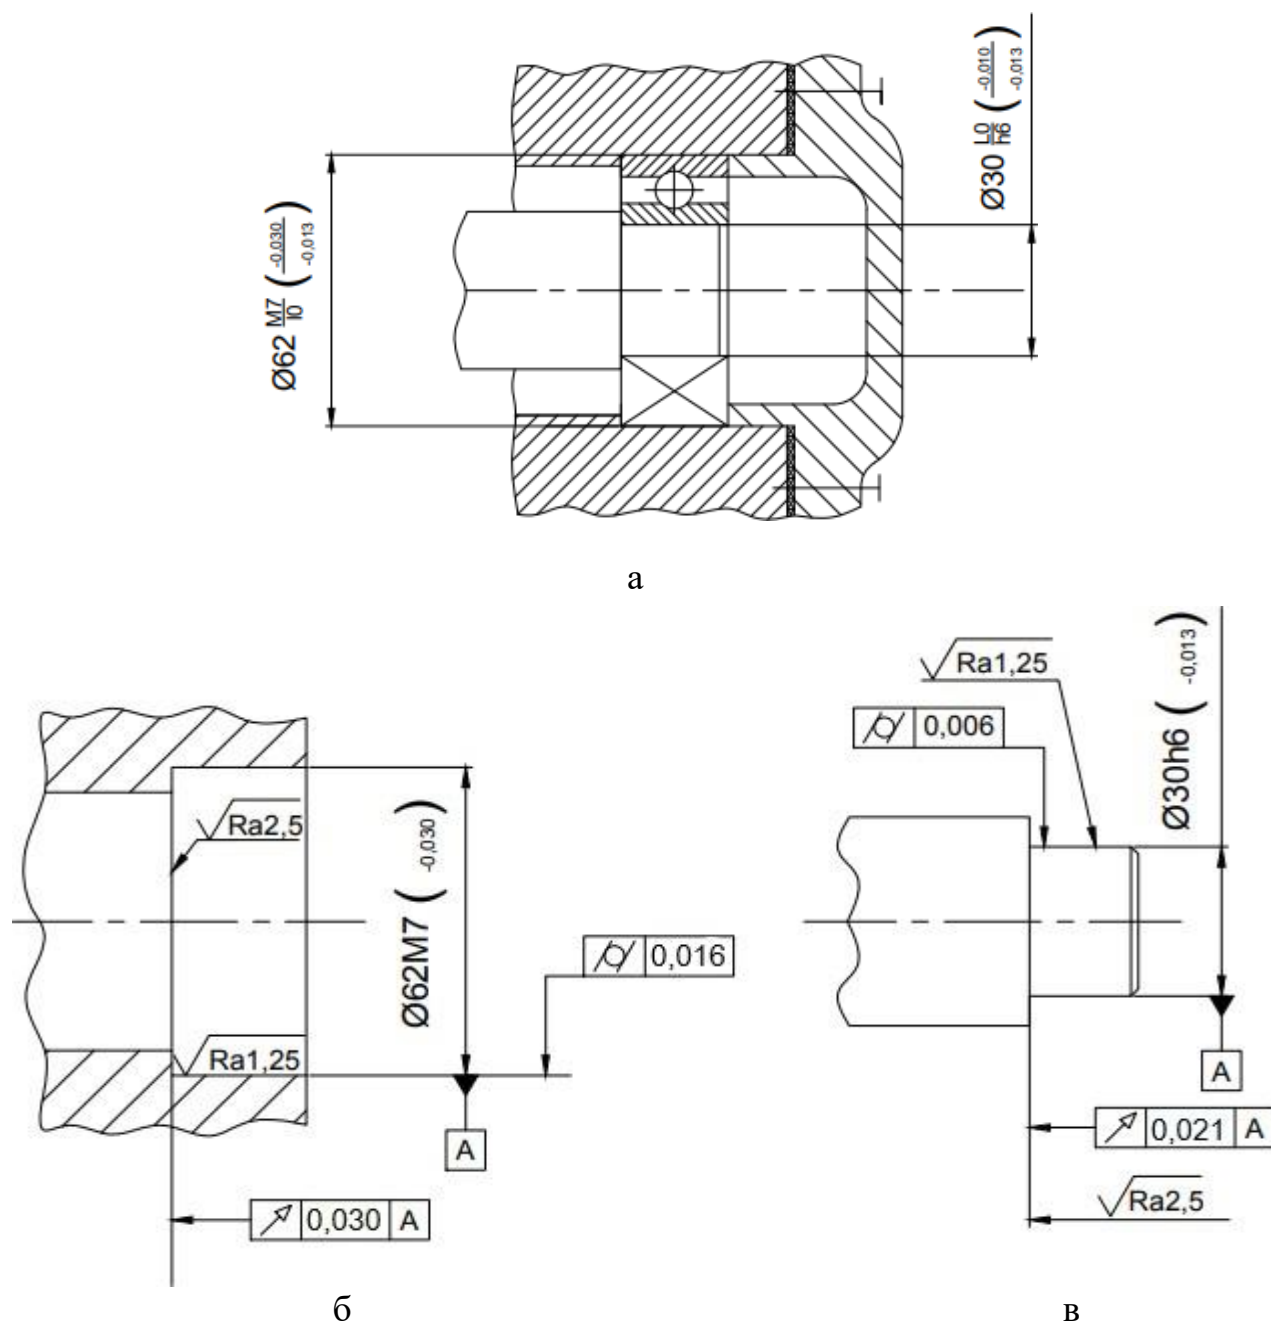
Эскизы подшипникового узла (а) и деталей сопрягаемых с подшипником (б – отверстие, в – вал)
